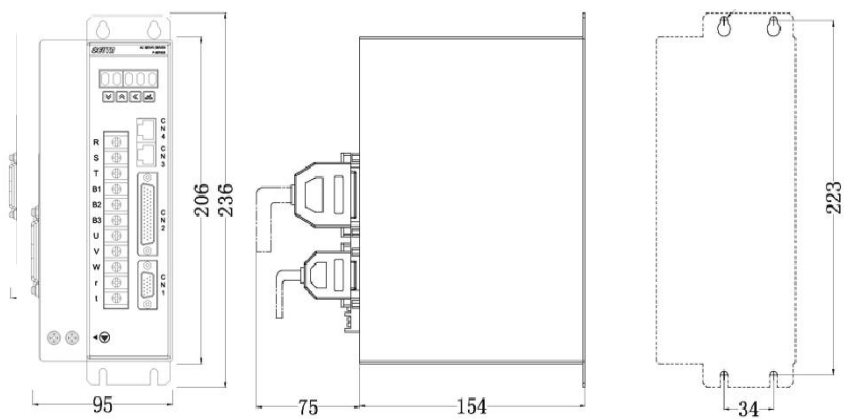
ID100 驱动器 B 型结构安装尺寸图
